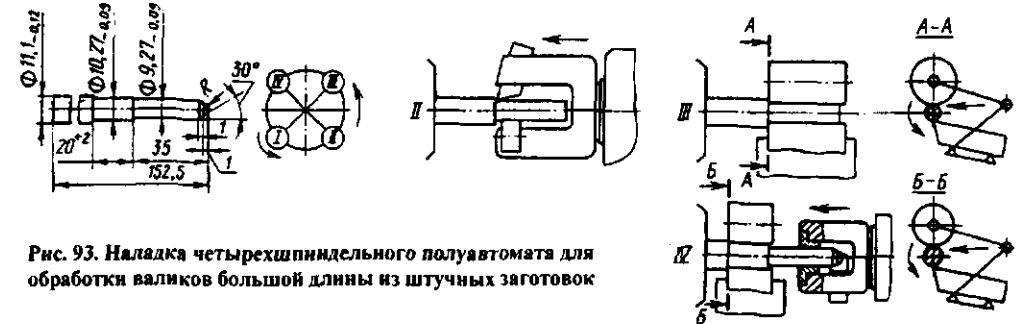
Наладка четырехшпиндельного полуавтомата для обработки валков большой длины из штучных заготовок
